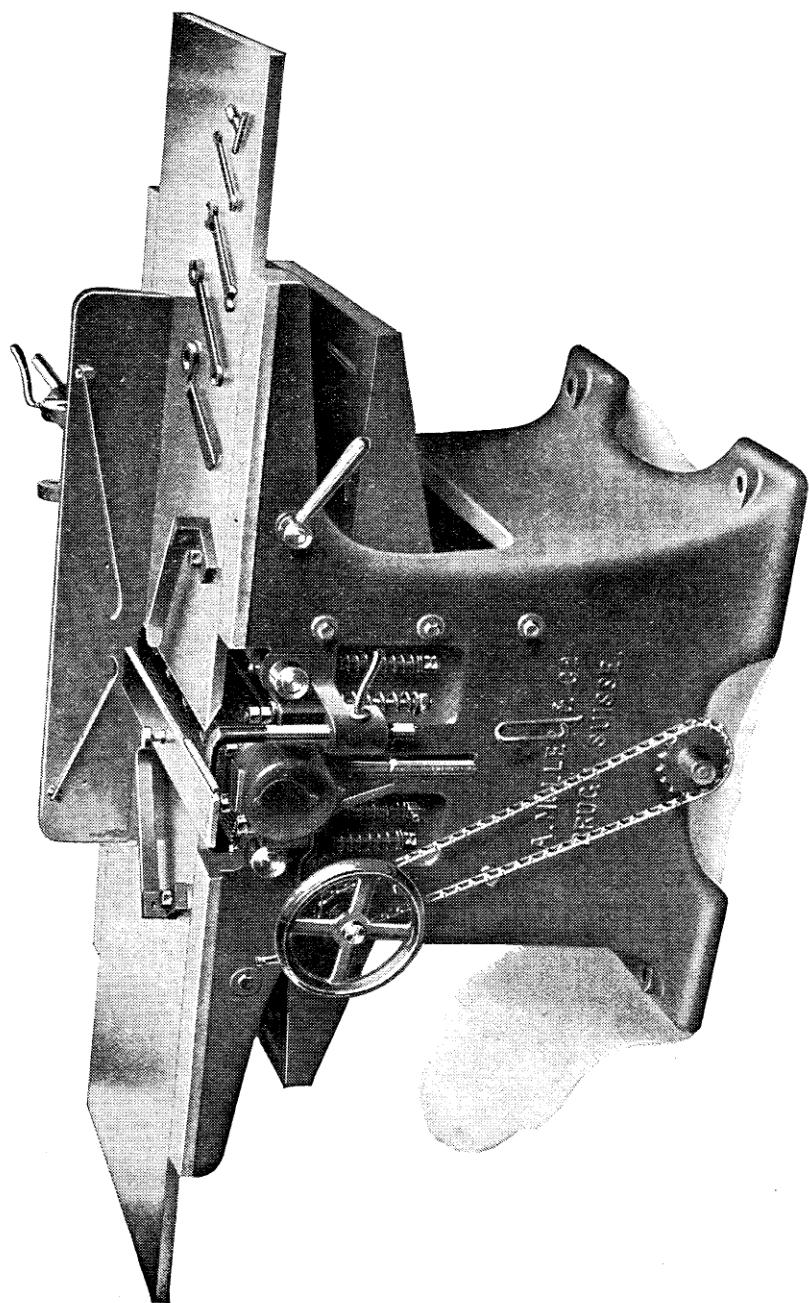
Machine combinée à dégauchir, moulurer et raboter en épaisseur.
